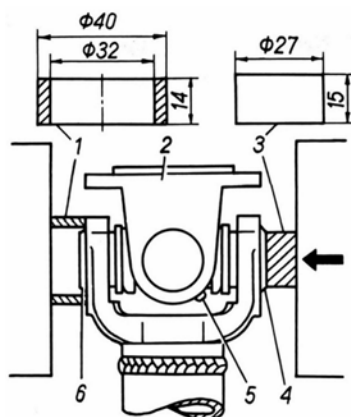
Разборка карданного шарнира: 1 – кольцо; 2 – фланец шарнира; 3 – оправка; 4 и 6 – подшипники; 5 – пресс-масленка
